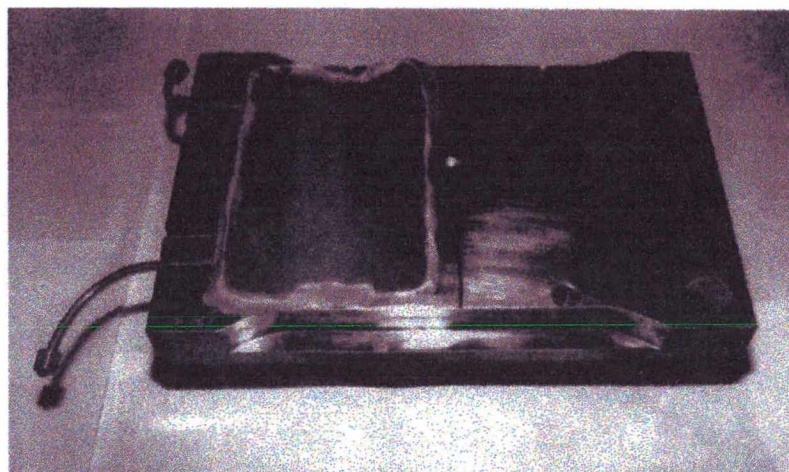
Montagem do inserto no porta moldes com composto de epóxi misturado com alumínio na sua parte posterior (Decelles & Barritt., 1996)
